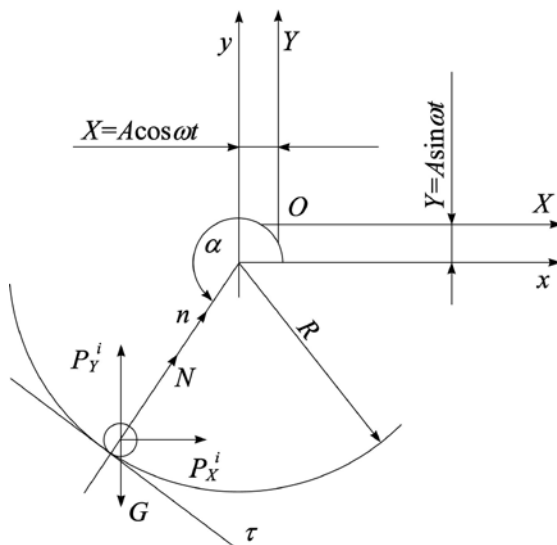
Взаємодія абразивної частинки з оброблюваною поверхнею, яка здійснює коливні і поступальні рухи
